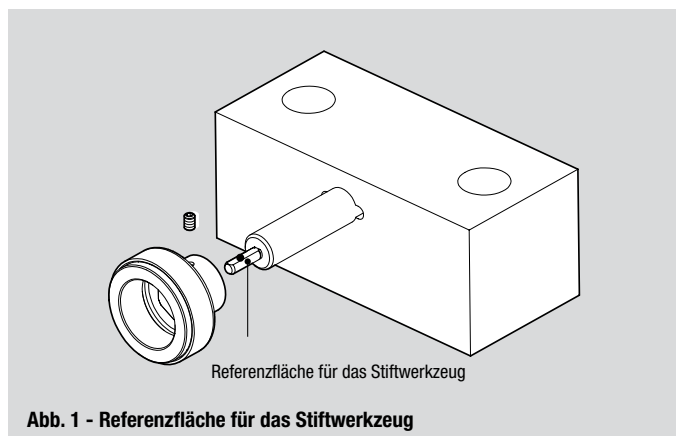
Referenzfläche für das Stiftwerkzeug
